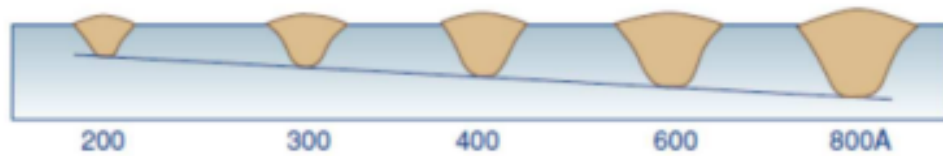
Вплив зміни зварювального струму на форму зварювального шва
